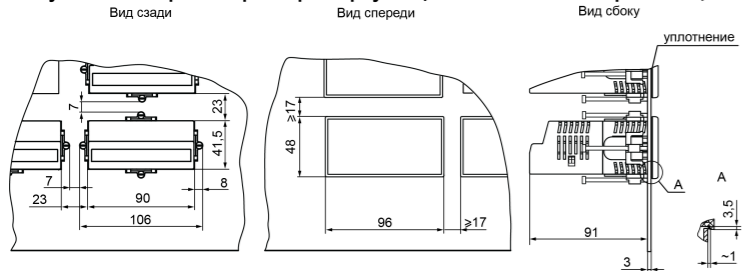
Корпус Щ2 в щите толщиной 3 мм
